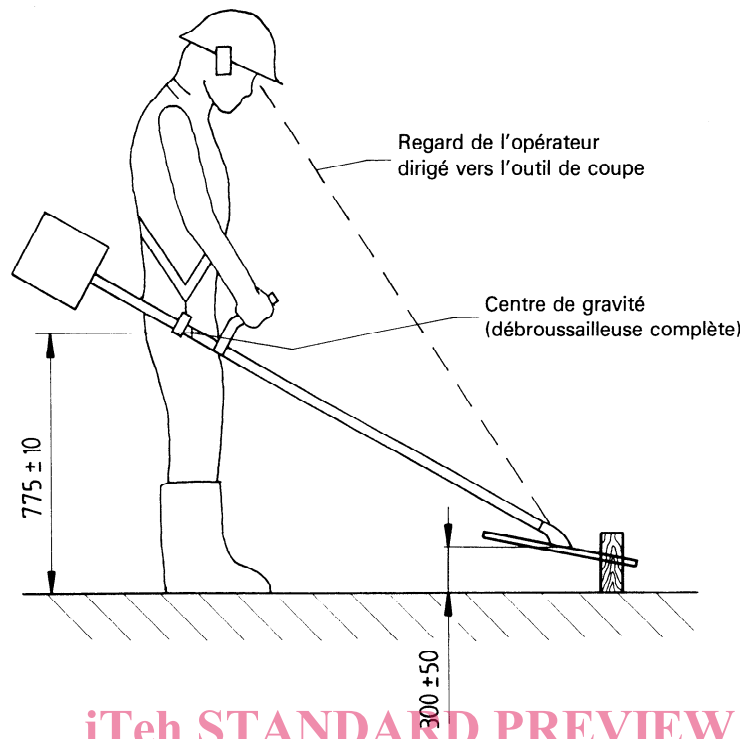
Position de la débroussailleuse pour l'essai de coupe
